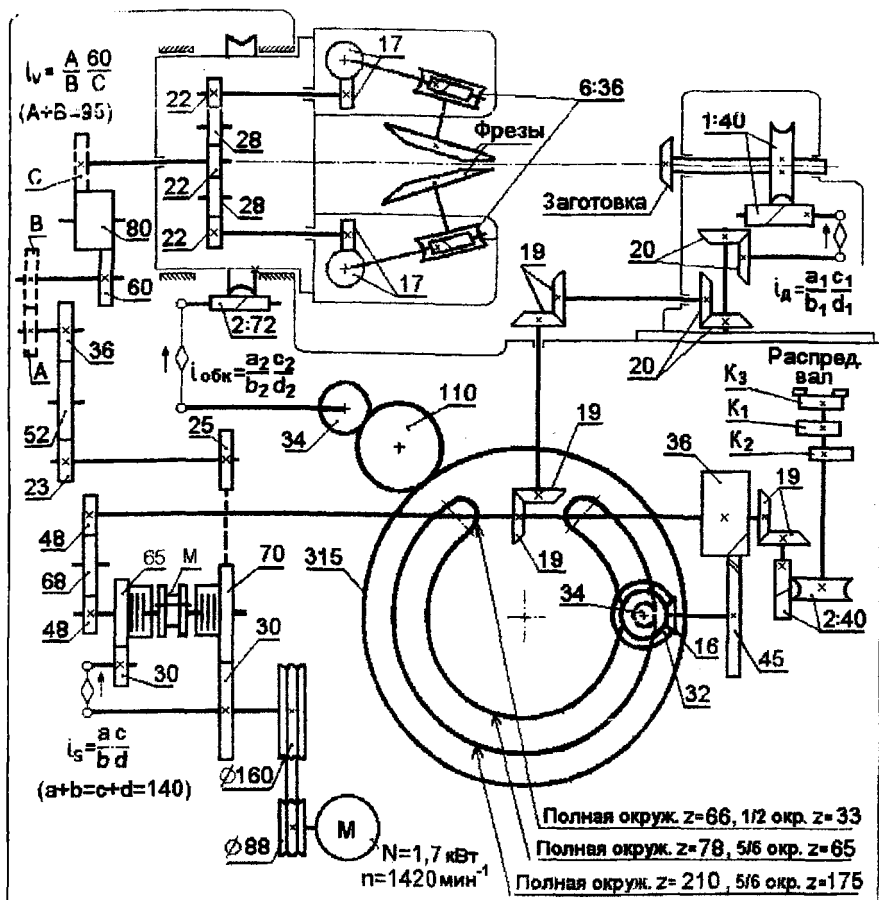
Кинематическая схема зубофрезерного полуавтомата модели 5П23
